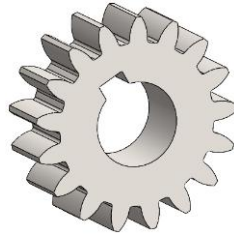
Modelo geométrico CAD 3D del engrane sol.
